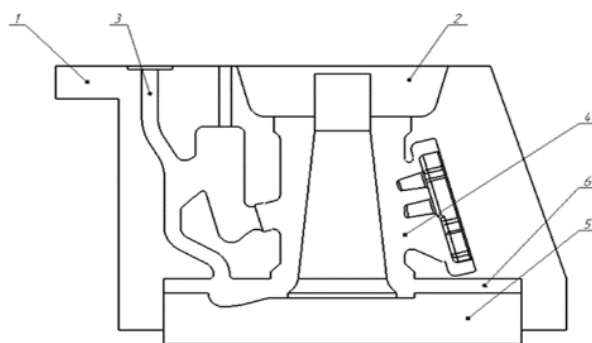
Устройство для изготовления тонкостенных отливок литьем в кокиль:
